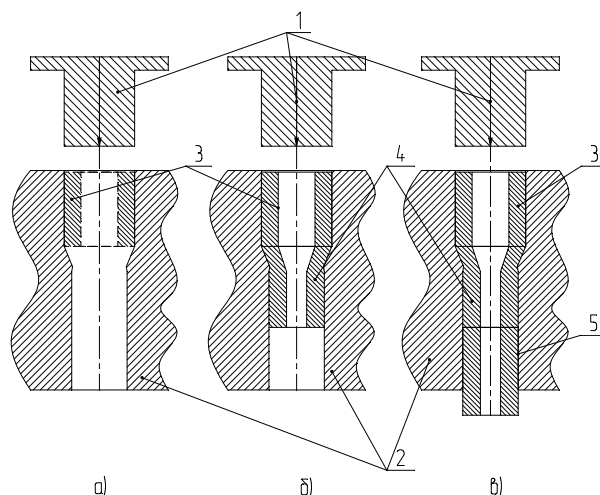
1-пуансон; 2-матрица; 3, 4,-деформируемые заготовки, 5-готовая поковка (деталь)
